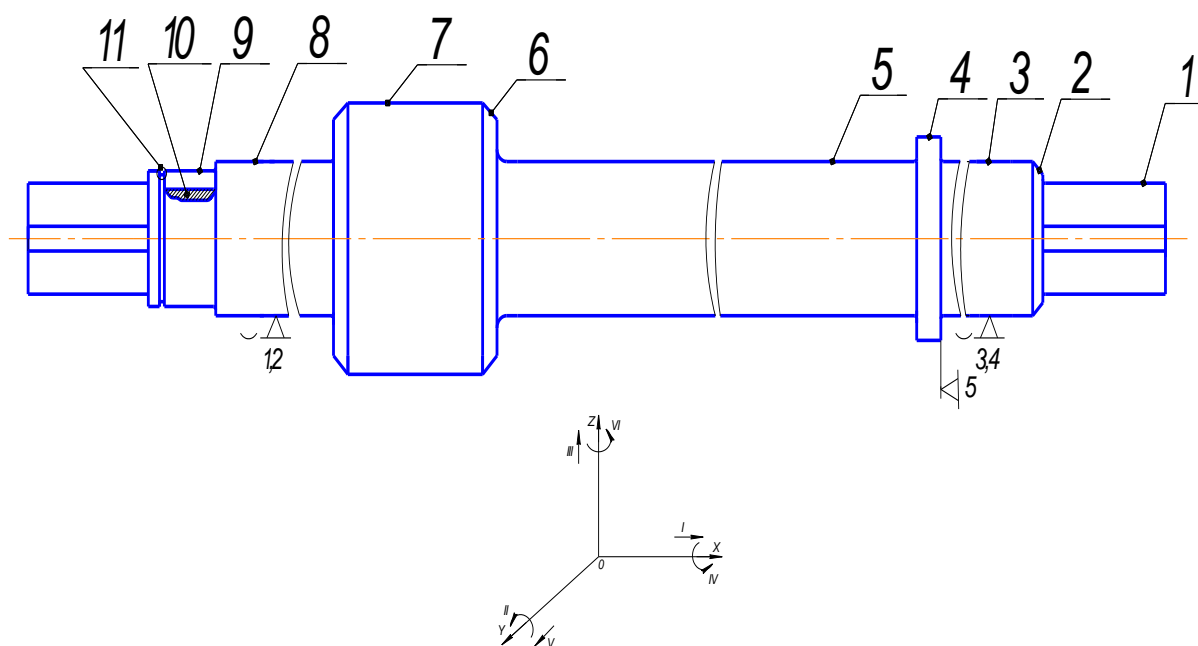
Эскиз детали с нумерацией поверхностей
